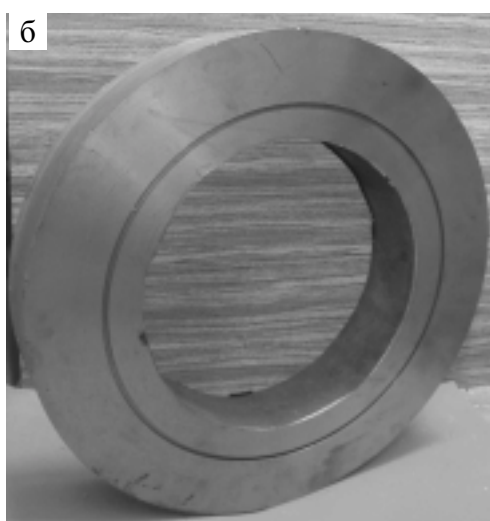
Прокатные валки (а) и торцевые уплотнения на барабанных ножницах для резки металла (б) с ЭЛН-покрытиями P6M5-TiCN.
